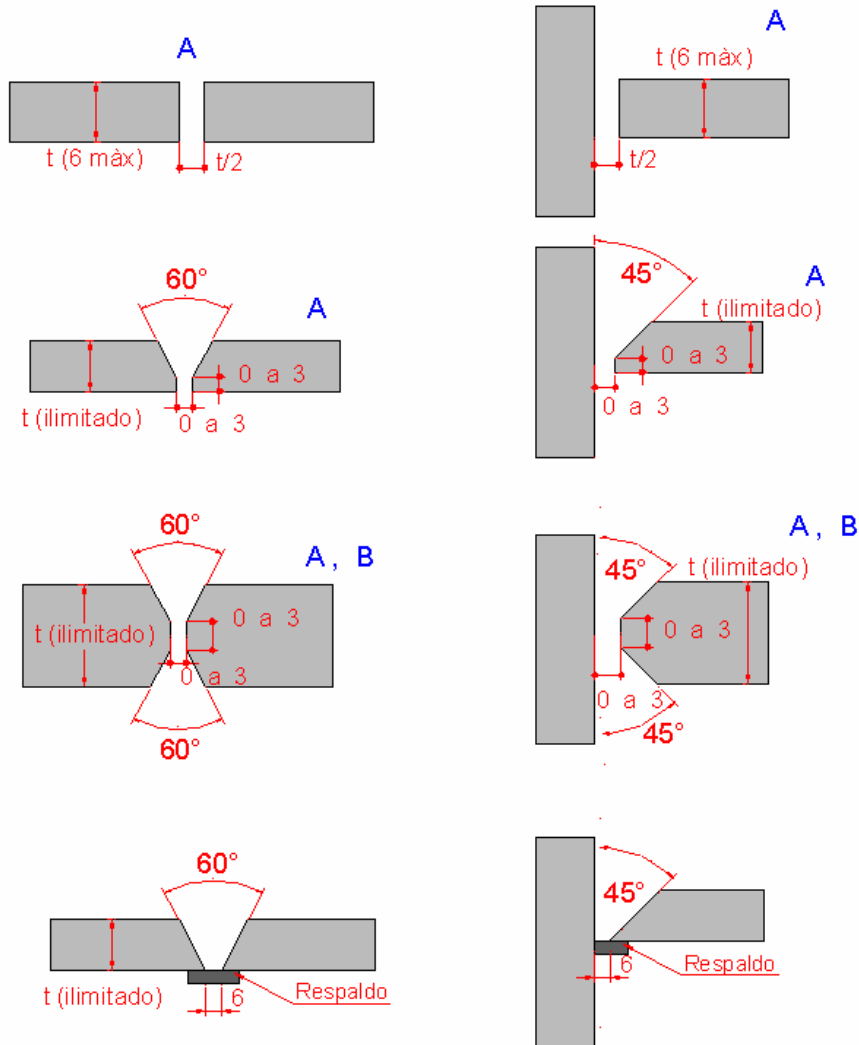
Detalles frecuentes de soldadura de penetración completa con electrodos recubiertos
